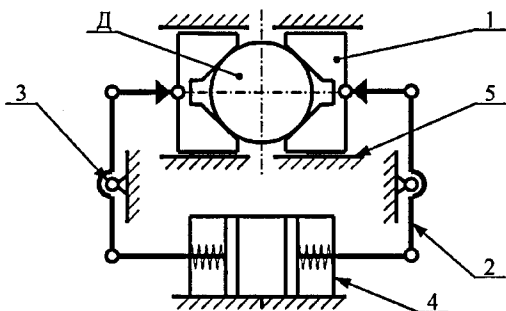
Пристосування на основі подвійного пневмоциліндра однобічної дії: 1 – центрувальні призми; 2 – важільний затискач; 3 – шарнірні опори, 4 – пневмоциліндр, 5 – корпус
